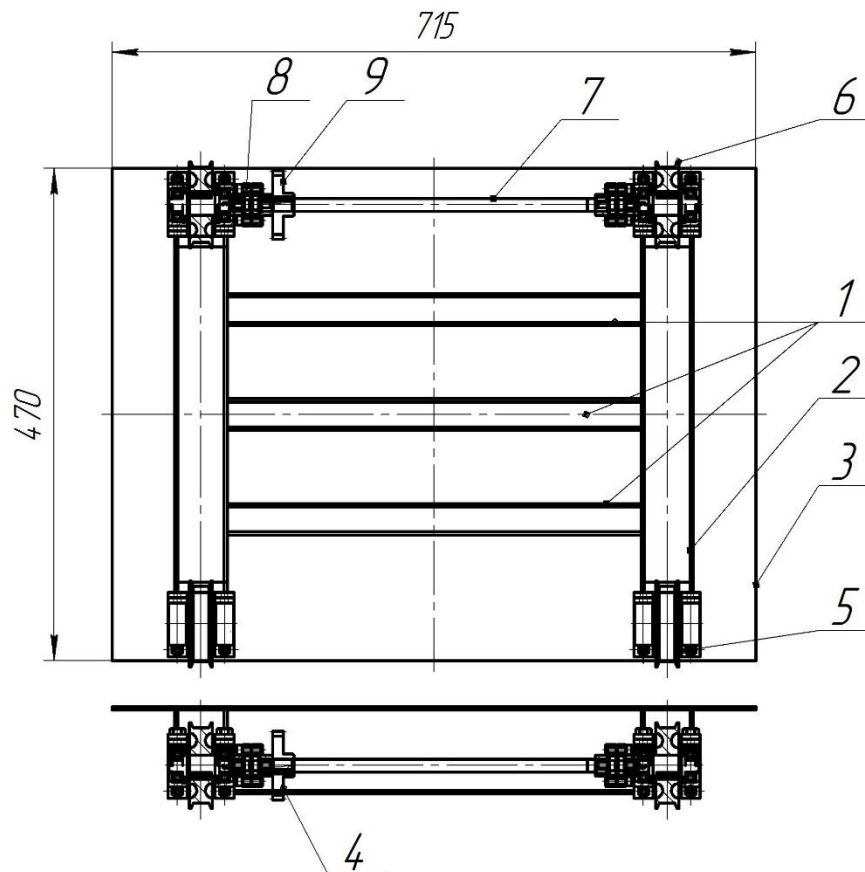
Вантажний візок мостового крану: 1 – поперечні зварні балки; 2 – поздовжні зварні балки; 3 – лист; 4 – привід переміщення візка; 5 – непривідне колесо; 6 – привідне колесо; 7 – трансмісійний вал; 8 – Муфта МУВП; 98 – зубчате колесо.
